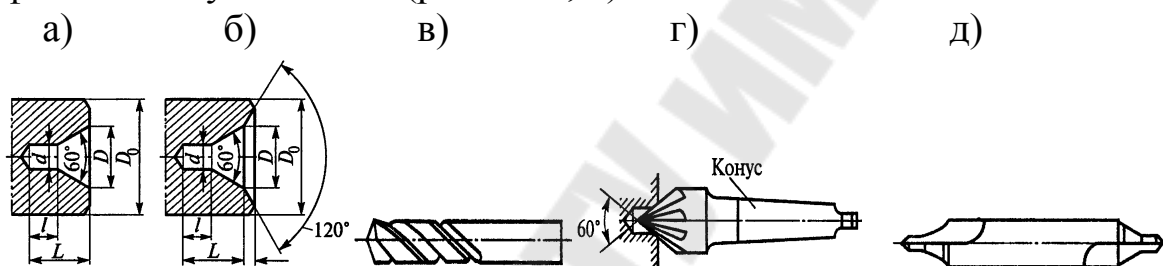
Конструкции центровых отверстий (а, б) и примеры центровых инструментов: в – цилиндрическое сверло; г – многозубая зенковка; д – комбинированное сверло с предохранительной фаской
